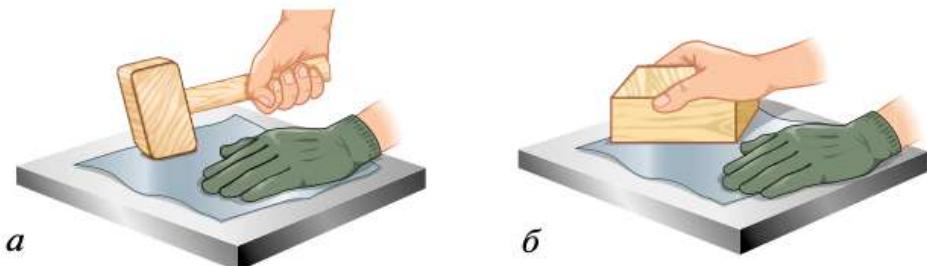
Правка заготовки из тонколистового металла на плите: а — киянкой; б — бруском
